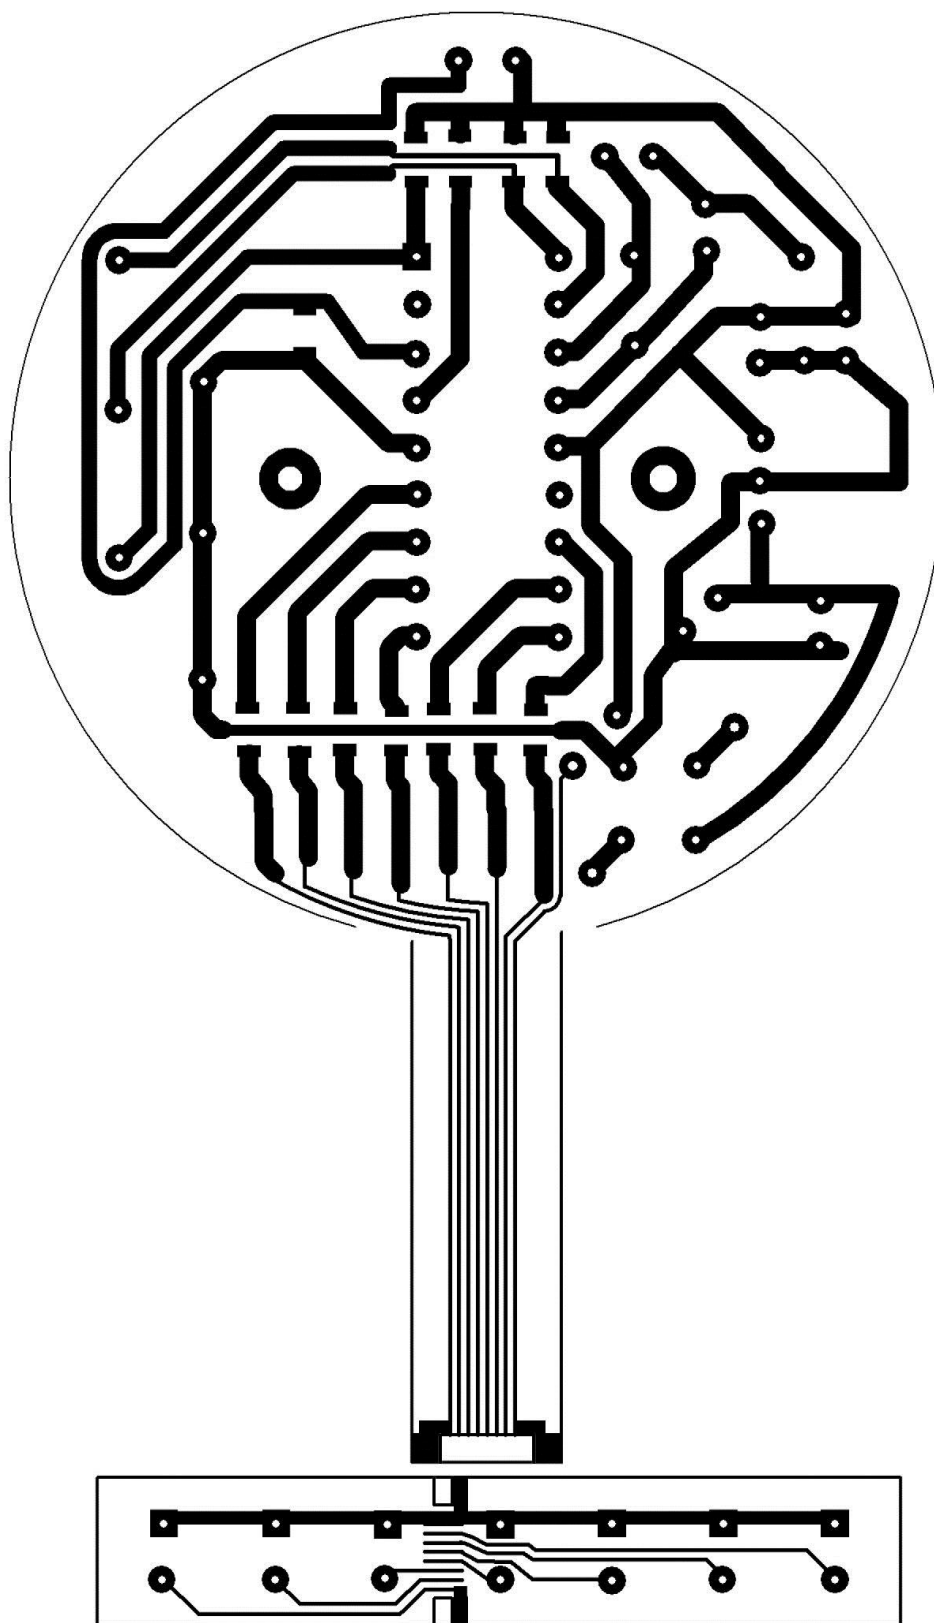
Печатная плата вращающейся части (маска для травления).
